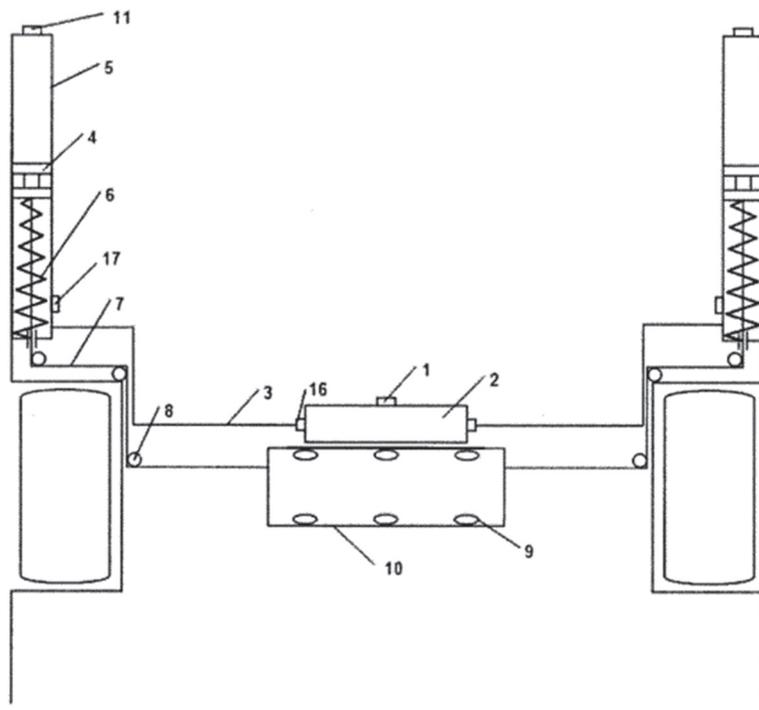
Устройство для предотвращения опрокидывания транспортного средства, общий вид: 1 – датчик положения кузова; 2 – ресивер со сжатым воздухом; 3 – пневмопатрубок; 4 – поршень; 5 – левый и правый пневмоцилиндры одностороннего действия; 6 – пружины; 7 – трос; 8 – блоки; 9 – ролики; 10 – противовес; 11, 17 – клапаны; 16 – клапан выпуска воздуха
